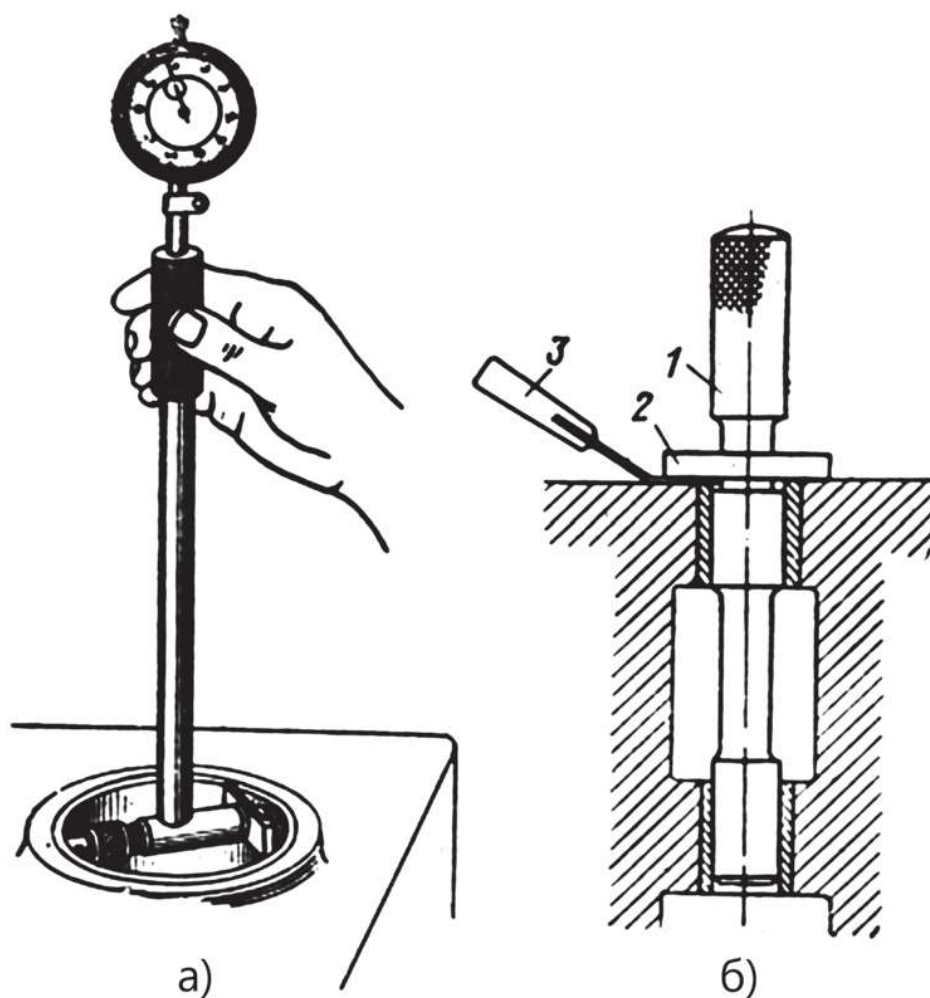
Проверка отверстий подшипника: а — проверка овальности индикаторным нутромером; б — проверка соосности отверстия калибром; 1 — калибр; 2 — буртик; 3 — щуп
